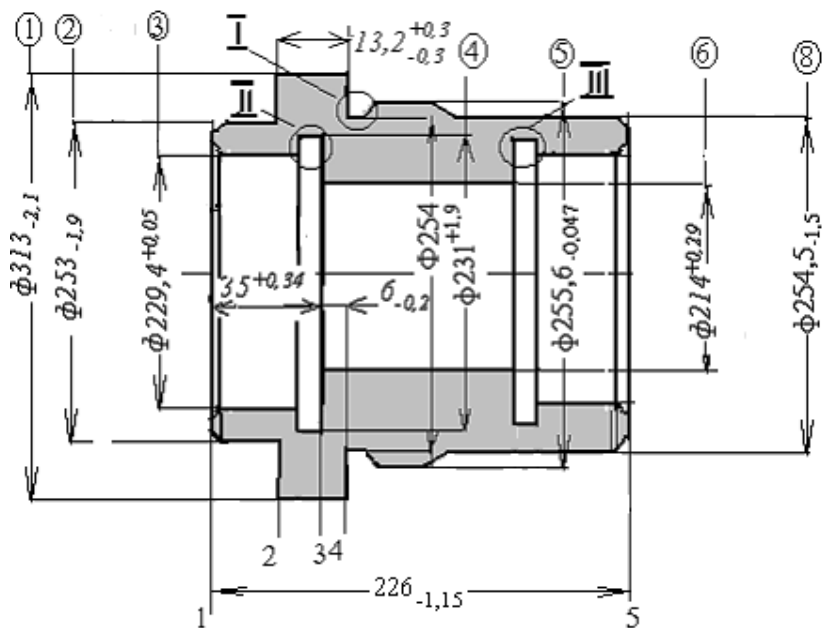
Чертеж заготовки «Коронная шестерня»
